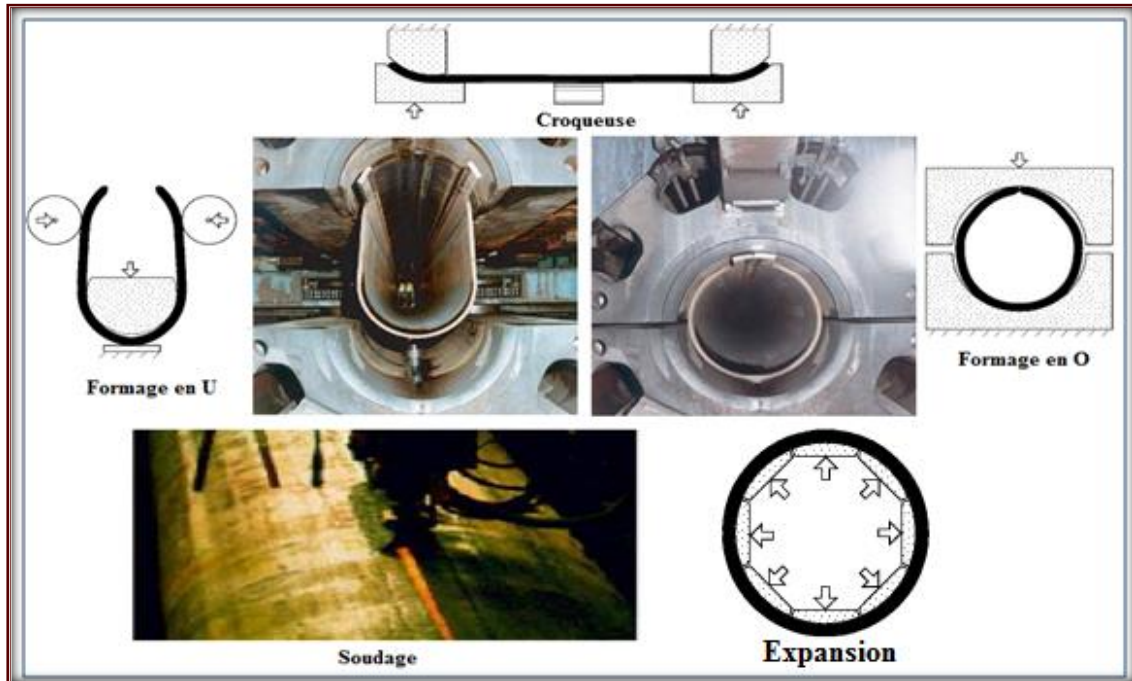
Etapes de fabrication des tubes soudés longitudinalement selon le procédé UOE [20].
